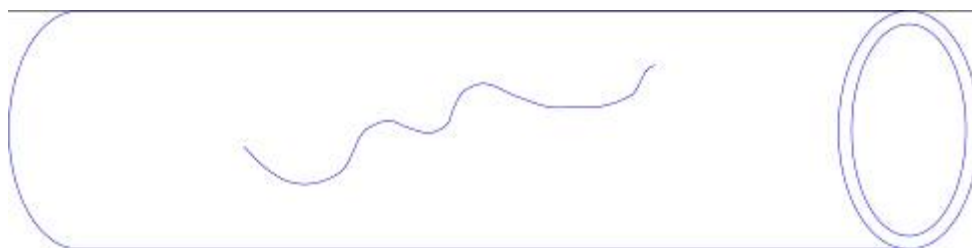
Локальная прокатная плена, расположенная на наружной поверхности трубы, образуемая при раскатывании непологой зачистки дефекта, имевшегося на заготовке
